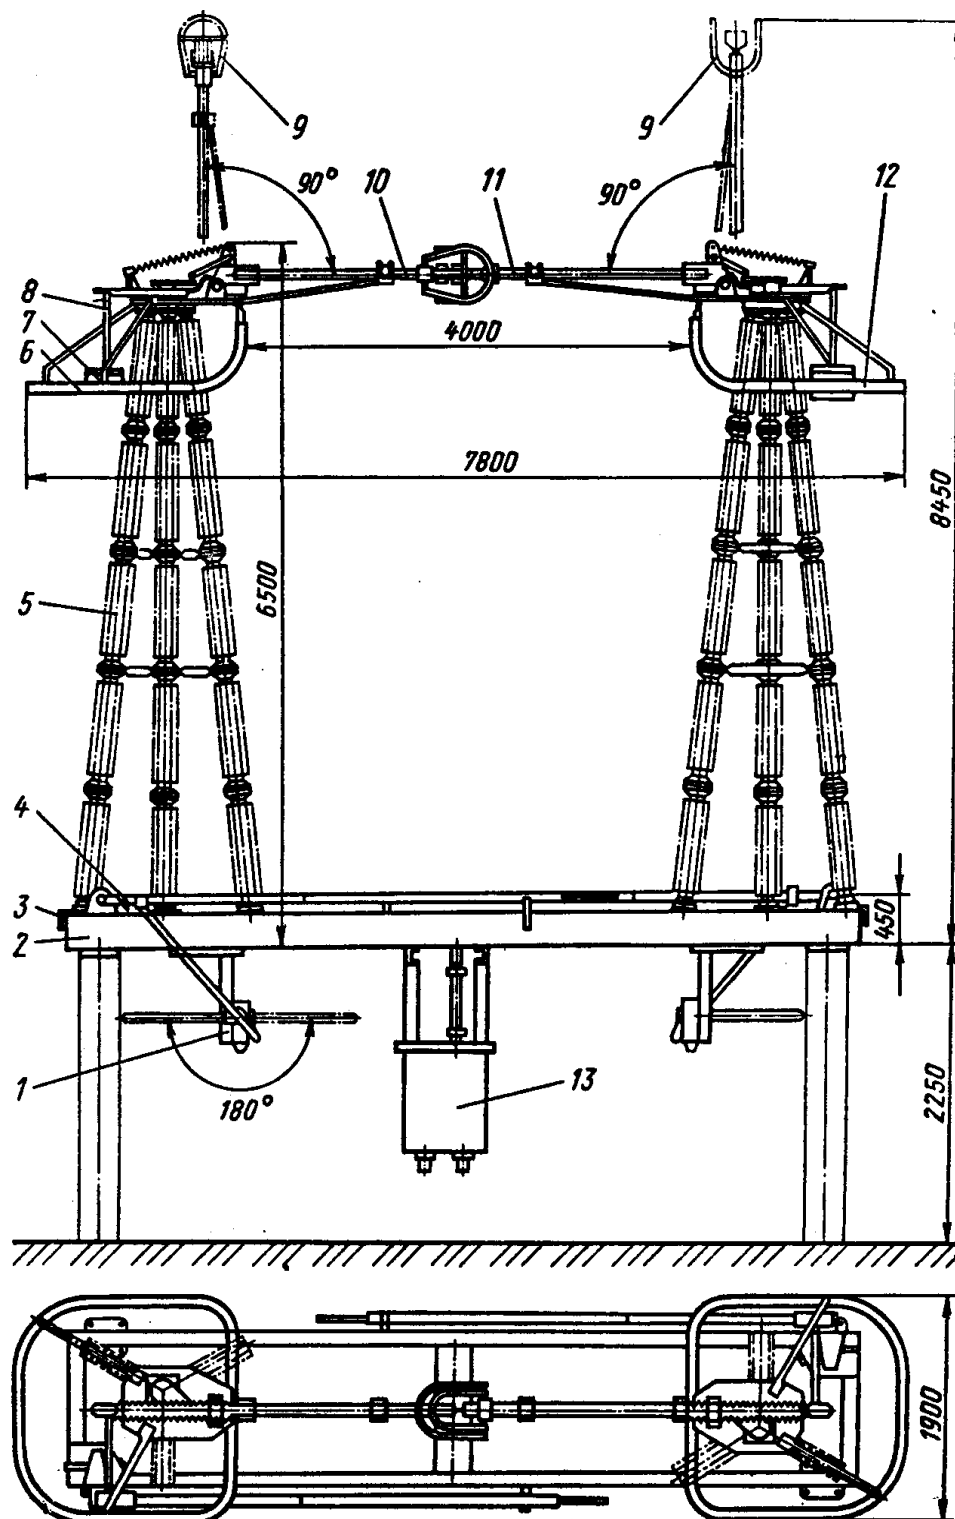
Роз'єднувач для зовнішньої установки
